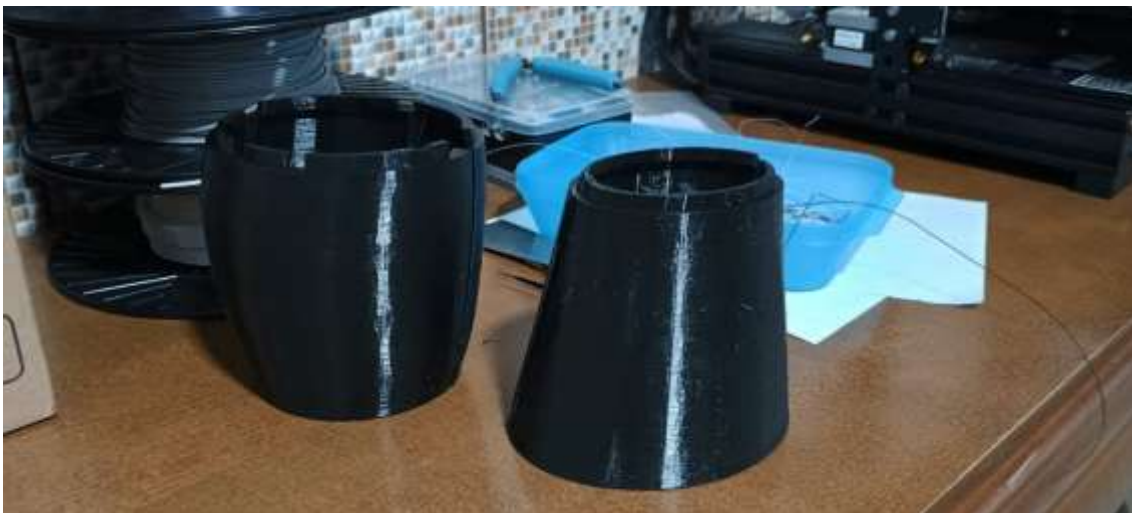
Foto da Impressão de parte do braço. – Foto dos autores - 17/9/2025.
